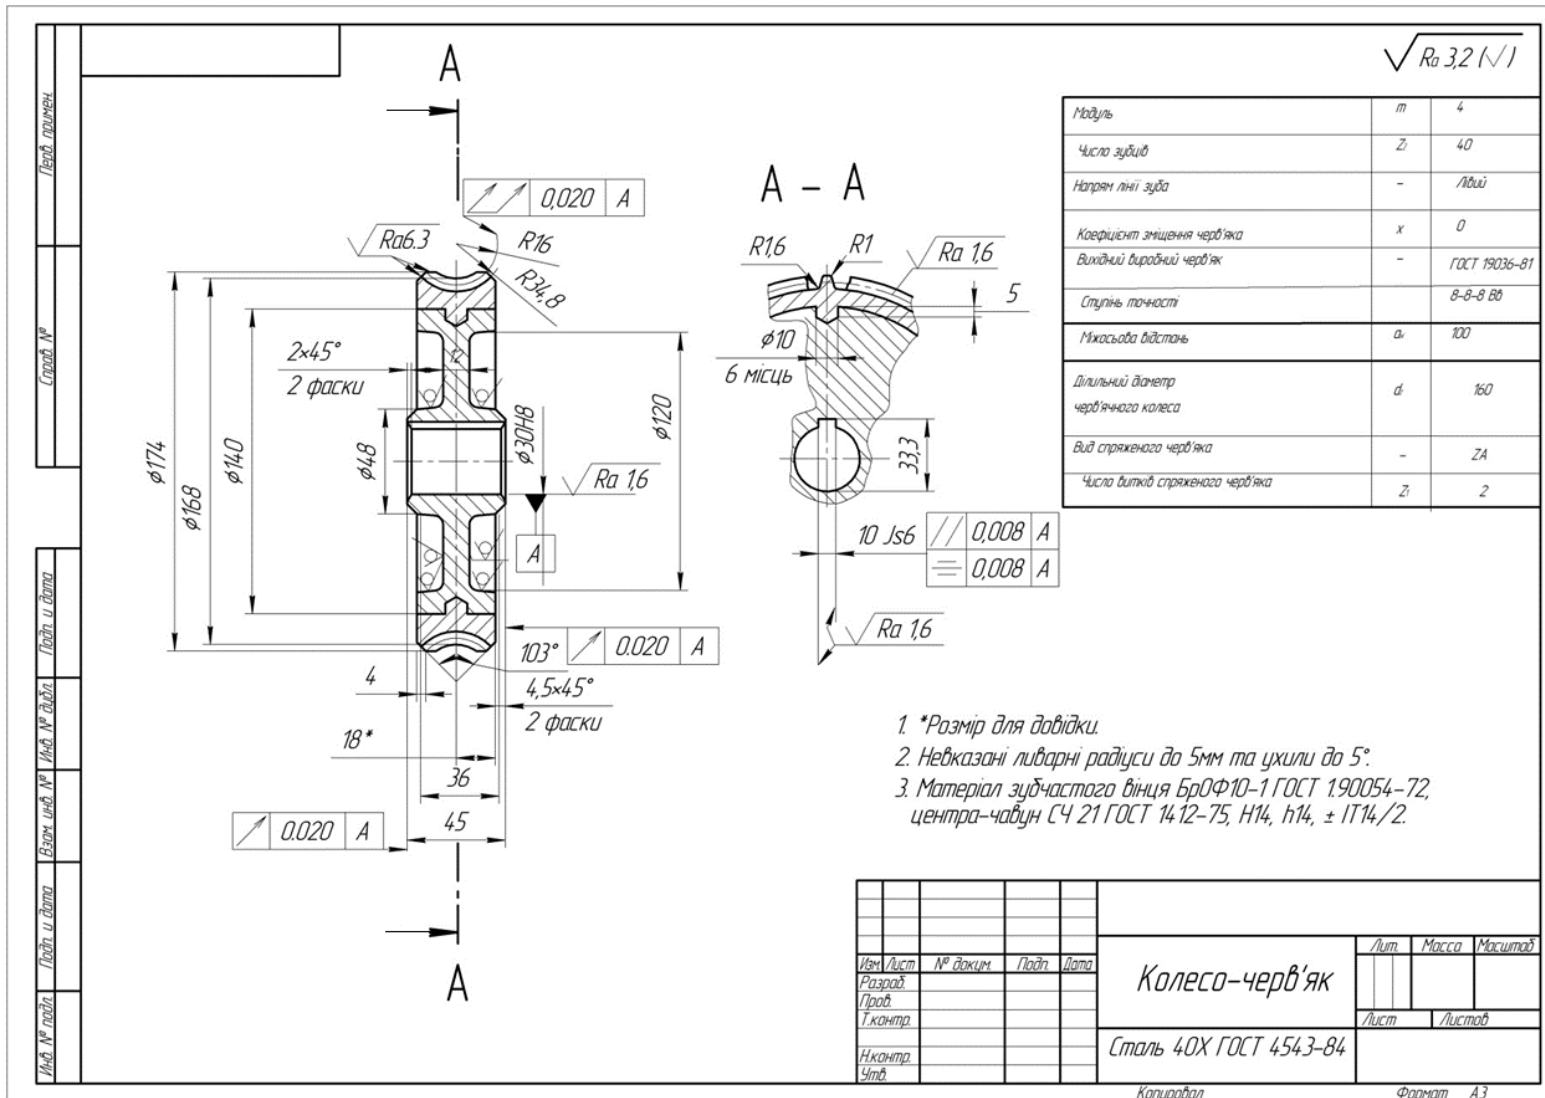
Робочий кресленник черв'ячного колеса
